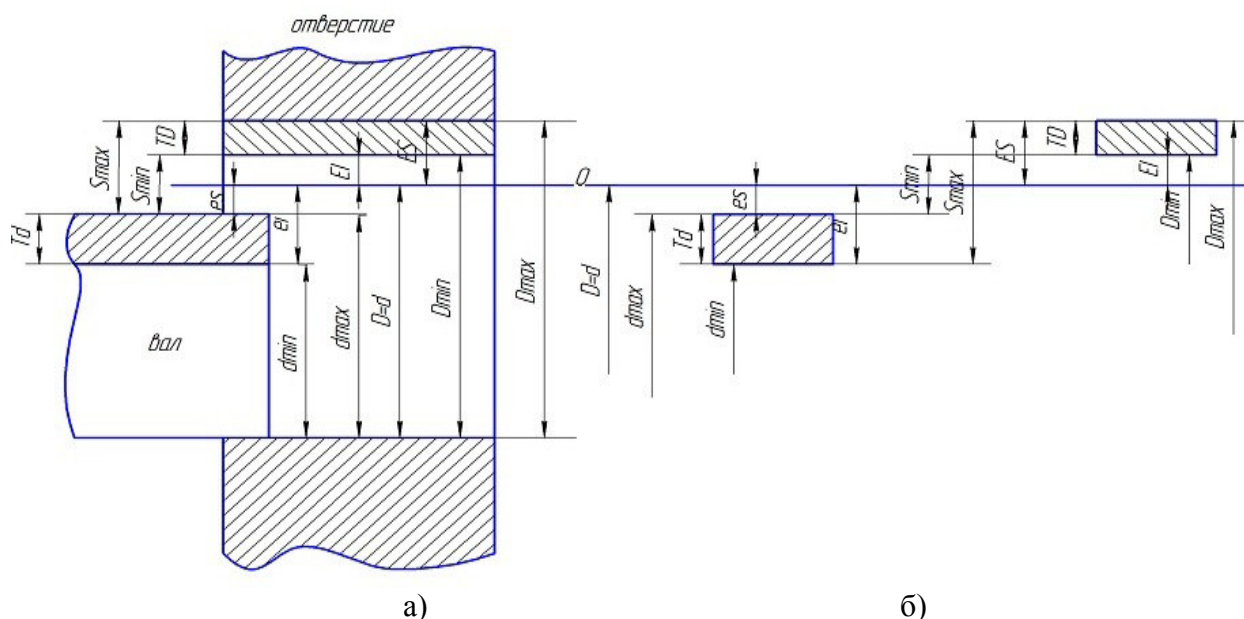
Посадка с зазором : а) схема сопряжения б) схема расположения полей допусков
